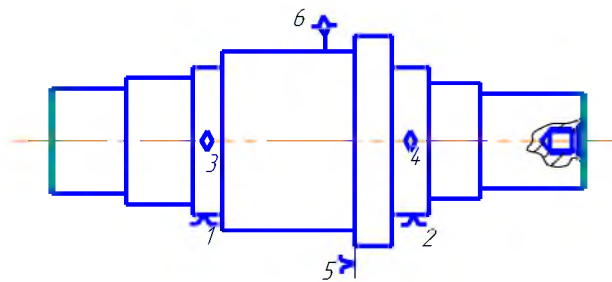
Теоретична схема базування деталі на фрезерно – центрувальній операції
